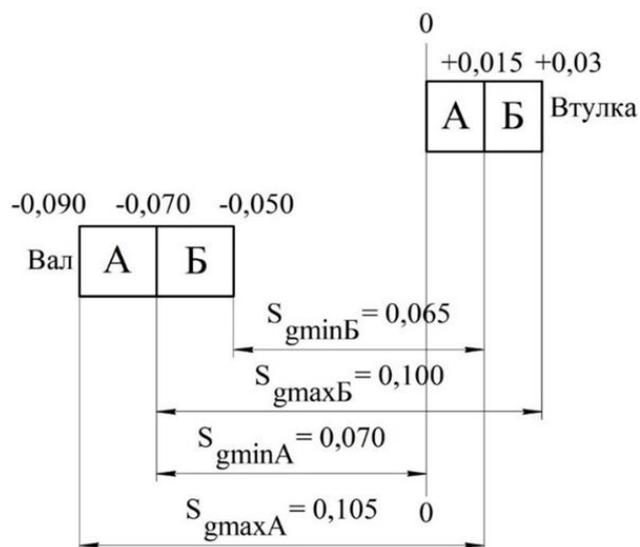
Схема расположения полей допусков при селективной сборке соединения «распределительный вал – втулка» двигателя ЯМЗ-236
